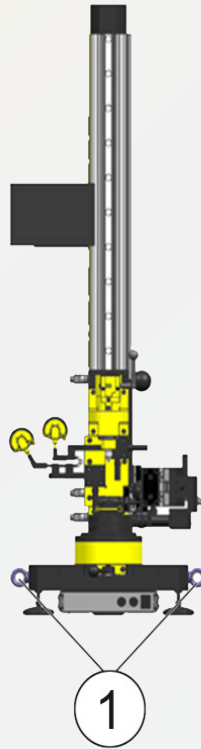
Aufnahmepunkte (1) für Ringschrauben
